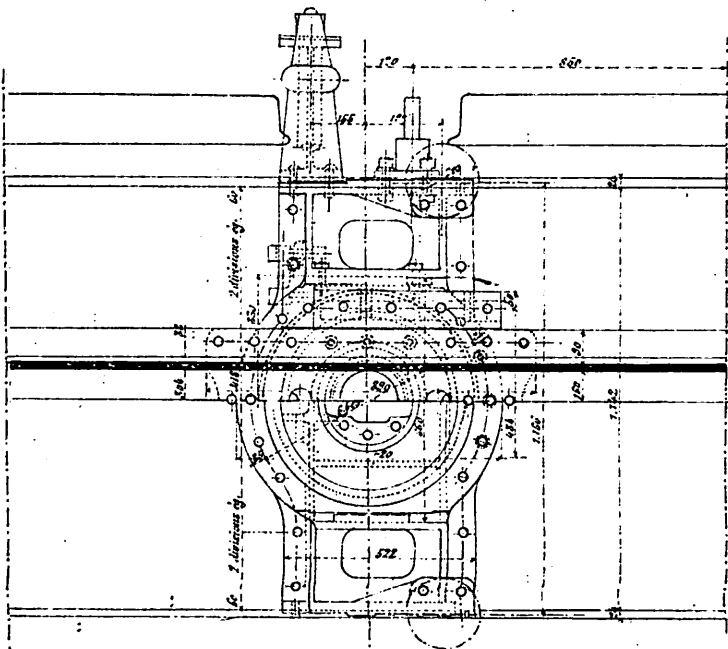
1/2 Coupe horizontale et 1/2 vue en plan
